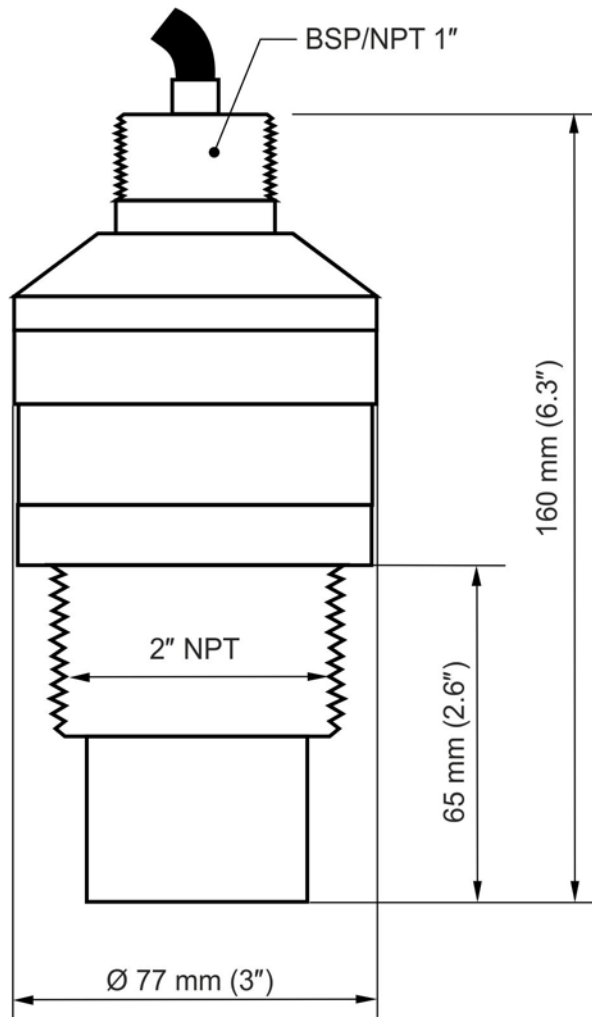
Abmessungen i-Sensor Typ 10 mit Einbaugewinde kabelseitig und optionalem Frontgewinde
